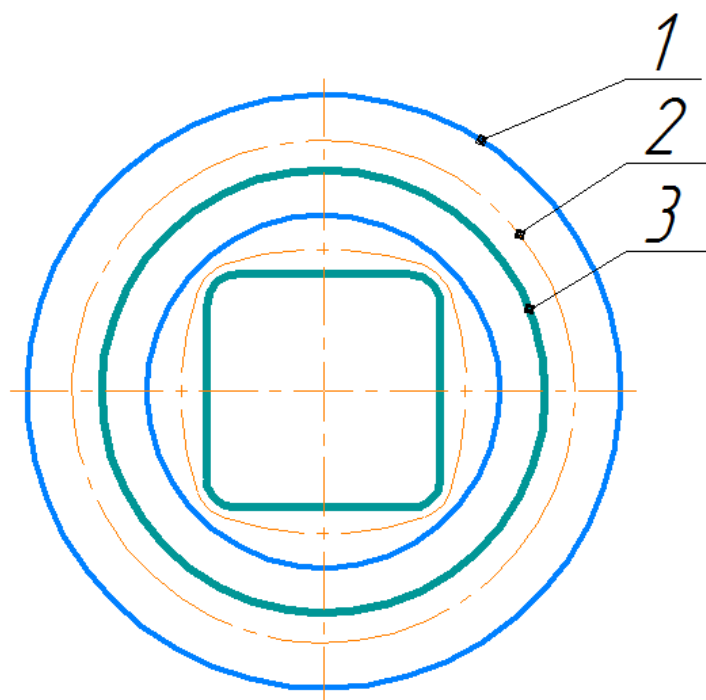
Двухпроходное волочение: круг –внутренний квадрат. 1- контур заготовки, 2 - контур промежуточного перехода, 3 – готовая труба.
